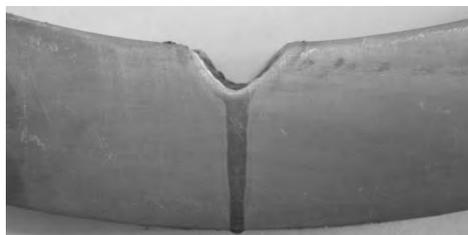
Макрошлиф сварного соединения, выполненного гибридной лазерно-дуговой сваркой
